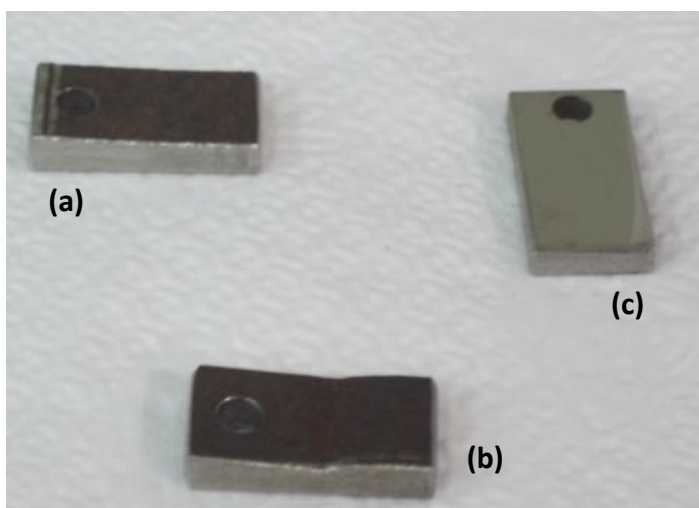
Imagem dos corpos de prova das três condições de superfície. (a) Metal de base (MB); (b) Junta soldada (JS); (c) Metal de base polido (MBP).
